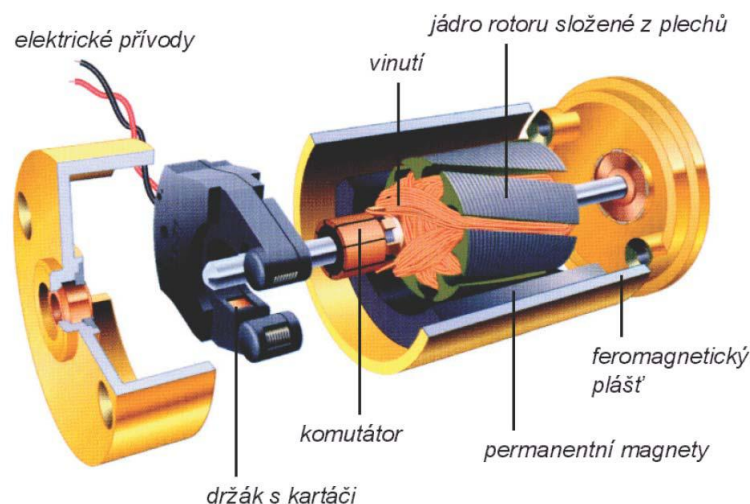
Hlavní části stejnosměrného elektromotoru [3]
